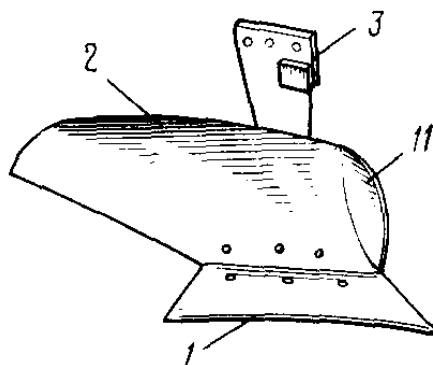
Схема корпуса для ромбической вспашки
